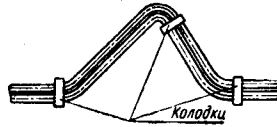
Схема распределения крепежных колодок на изогнутых участках трубопроводов.
